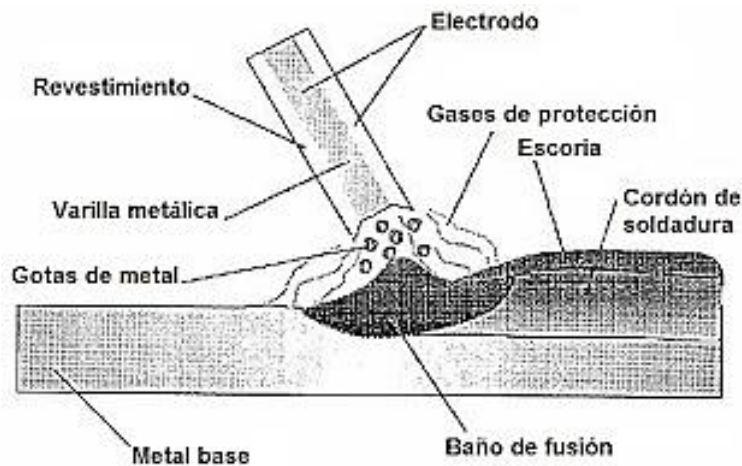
Diagrama esquemático del proceso de soldadura SMAW
